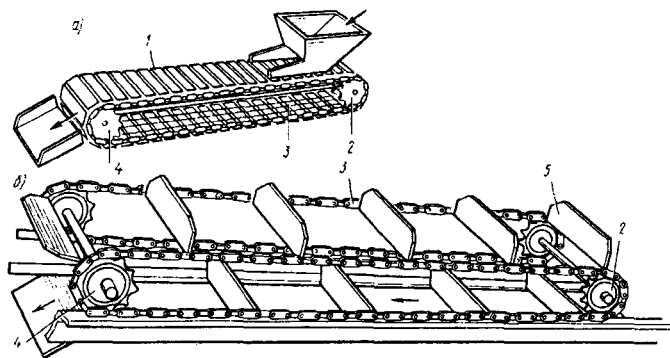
Конвейеры с цепным тяговым органом; 1 – пластина; 2 – натяжная звездочка; 3 – цепь; 4 – приводная звездочка; 5 – скребок.
